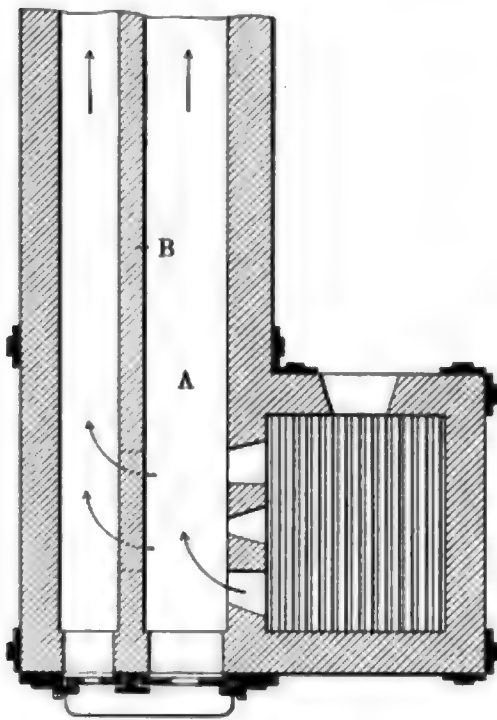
Rohrschweißofen mit Vorwärmer
